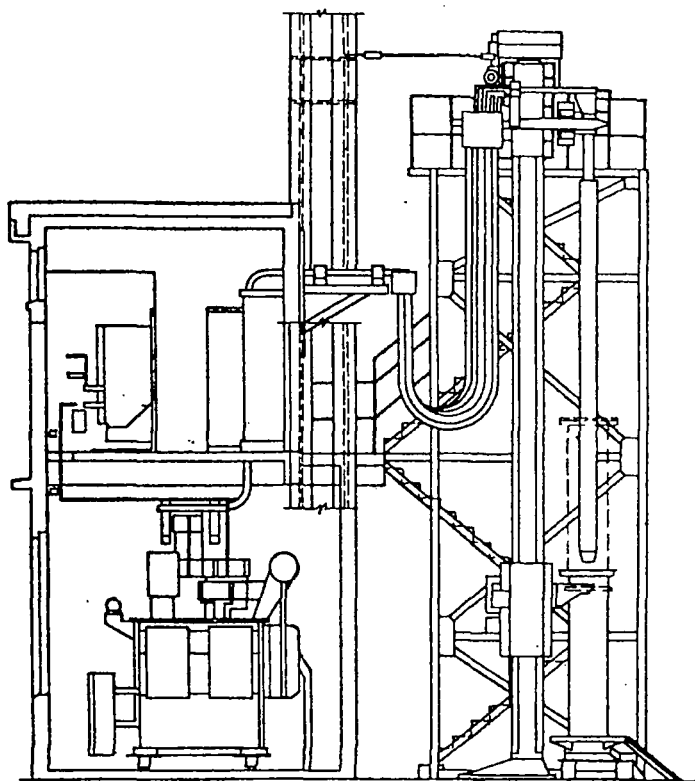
Схема печи электрошлакового переплава советской конструкции (Компани дез ателье э форж де ла Луар)
